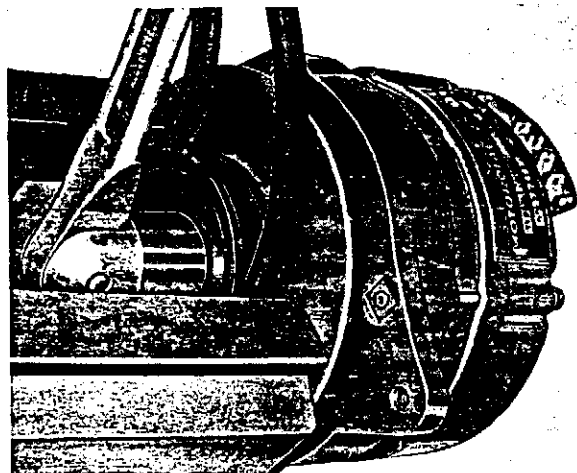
Ausbau der Mutter für die Riemenscheibe
